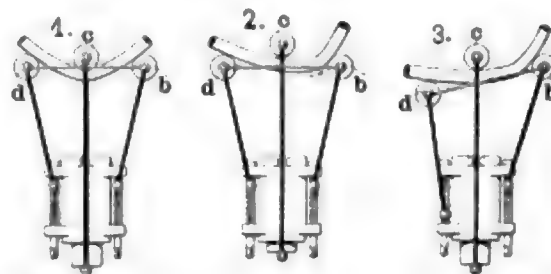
Z. A.: Hydraulische Rohrbiegemaschine von der Bonner Maschinenfabrik und Eisengießerei Fr. Mönkemöller & Cie. in Bonn-Dottendorf.
